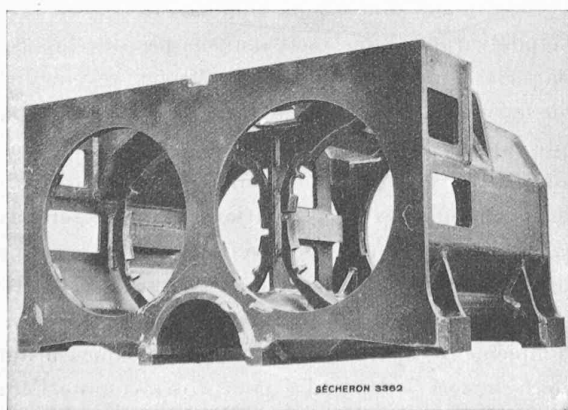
Carcasse soudée de moteur de traction.
